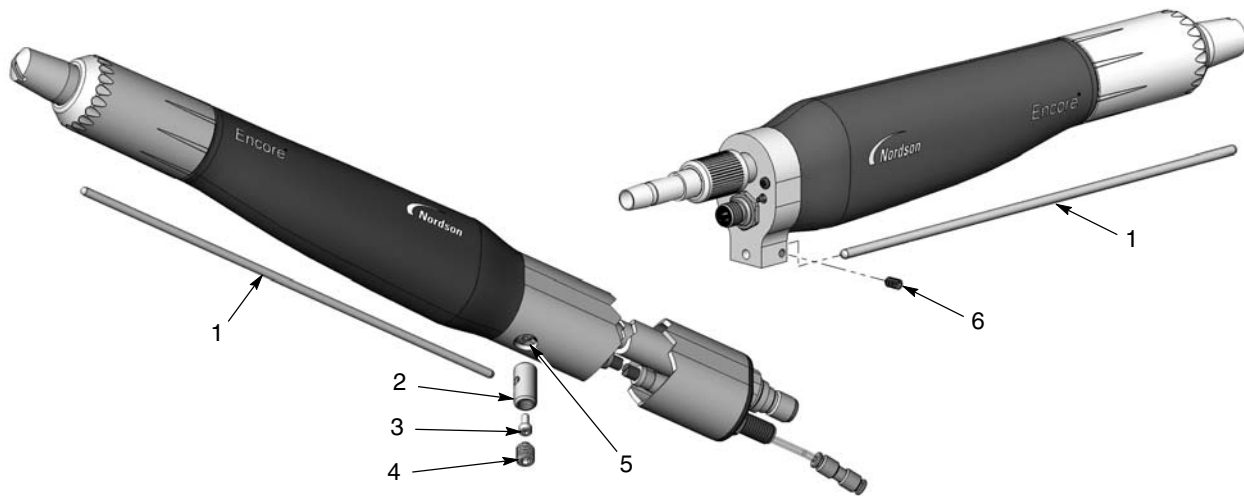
Montagem do colector de iões - pistola com barra de suporte ilustrada sem suporte articulado
